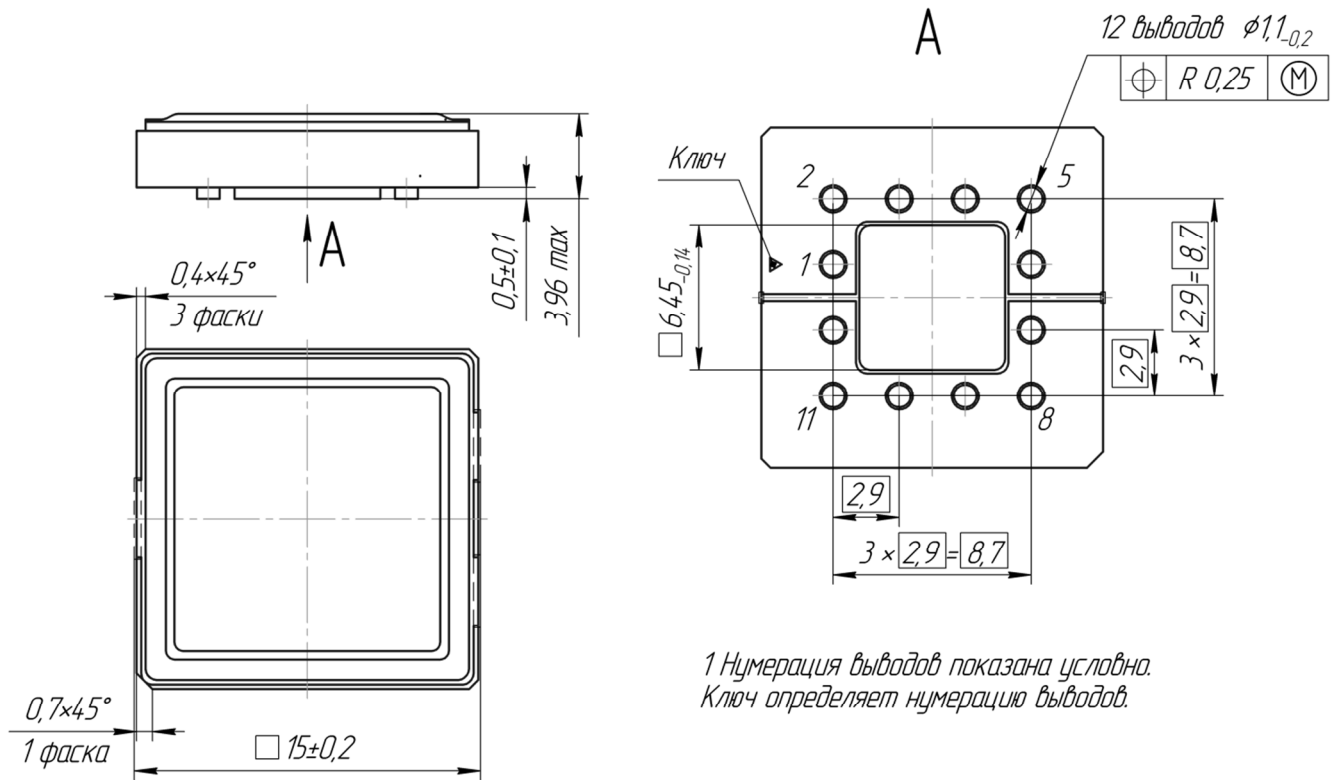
Габаритный чертёж корпуса МК КТ-119-1.
